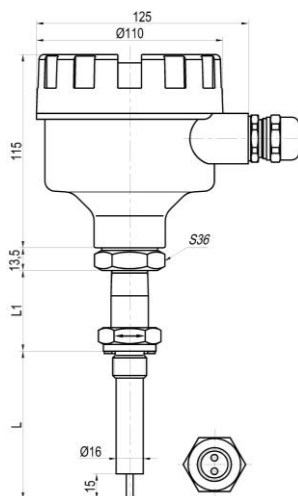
присоединение к процессу – штуцера с цилиндрическими резьбами
